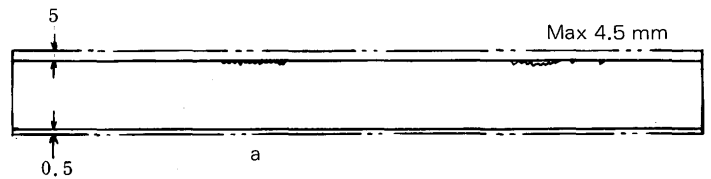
Schweißfläche: Eingußseite (b)
